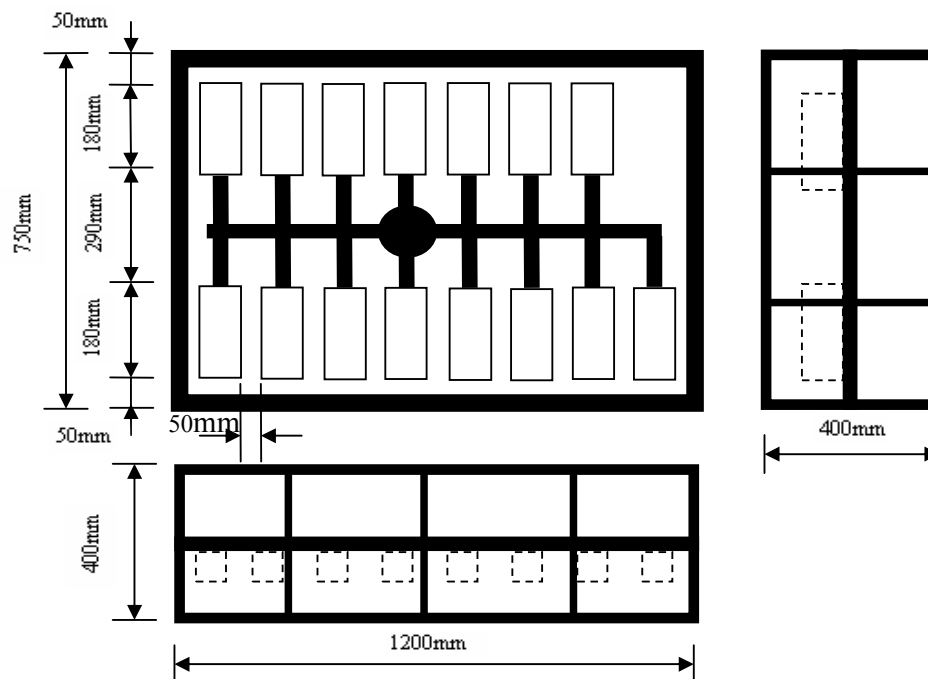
Desenho esquemático do molde e modelo para fundição dos corpos de prova do aço CA15.
